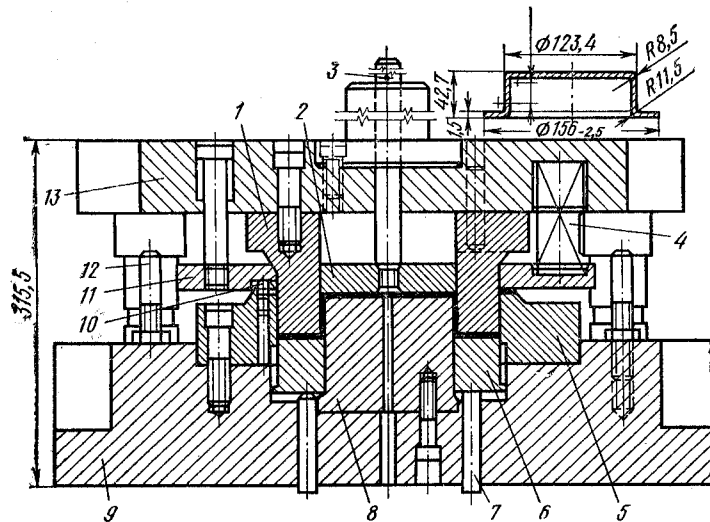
Комбинированный штамп для вырубki и вытяжки листовой заготовки
